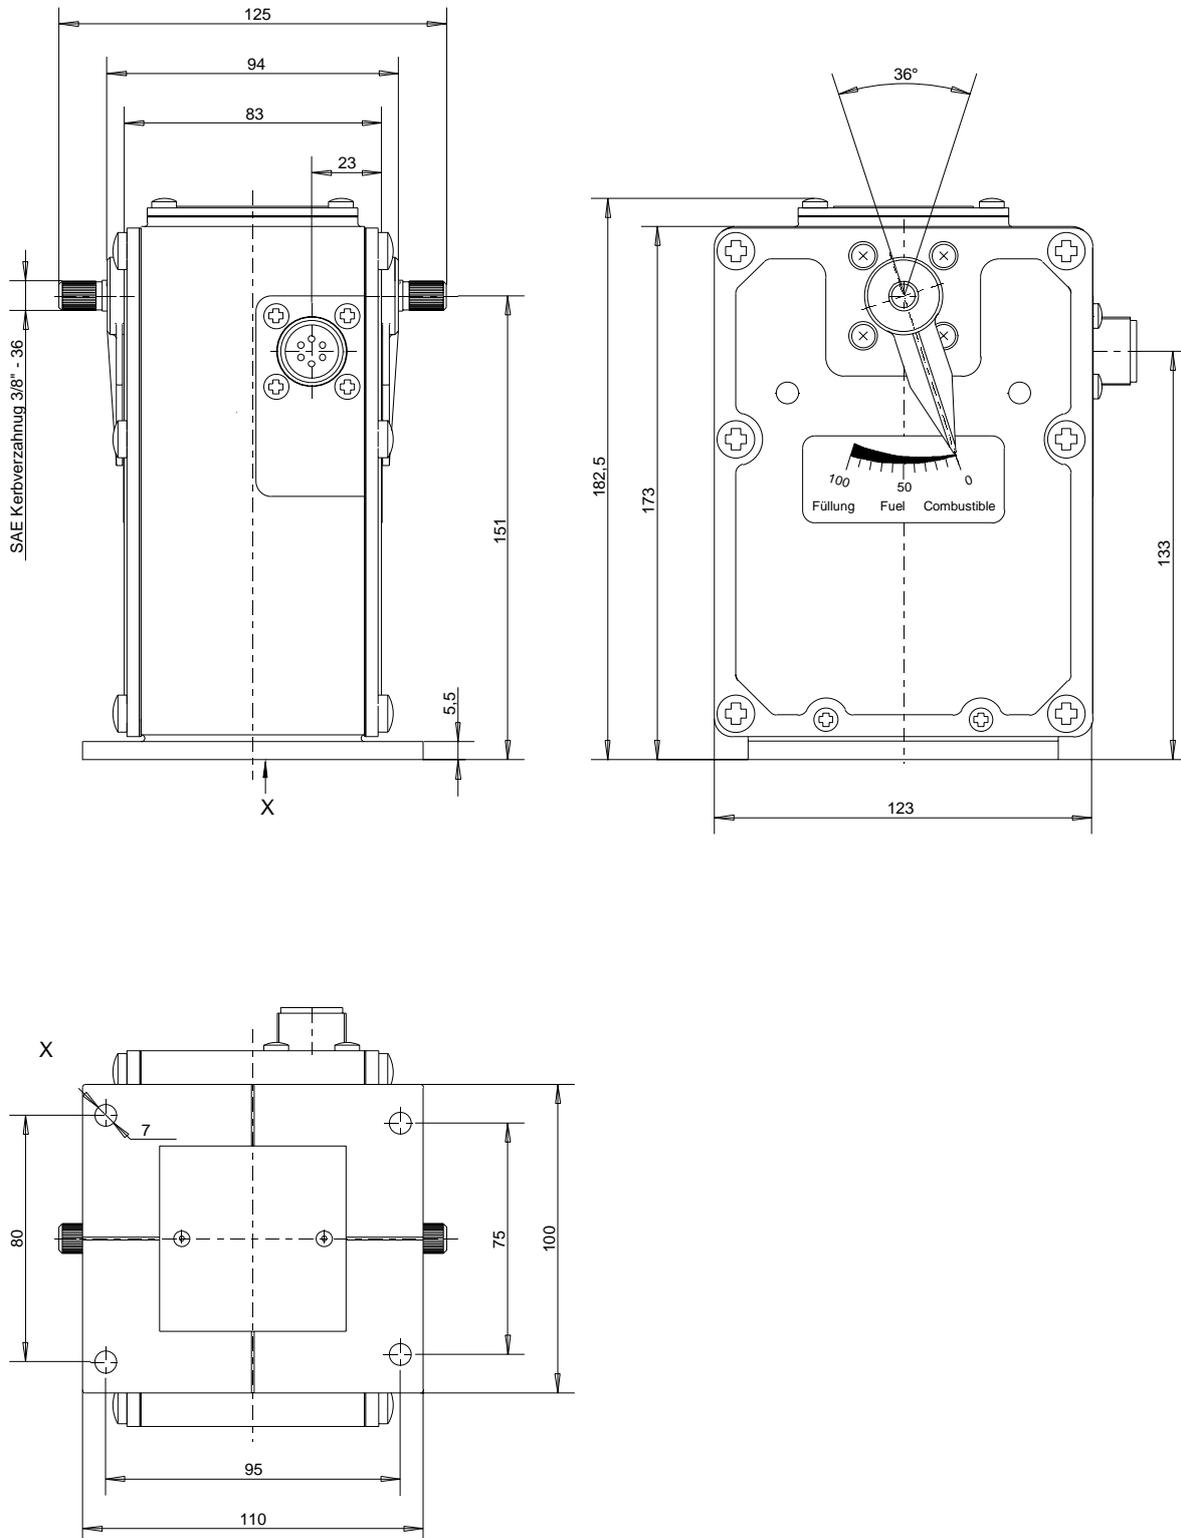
Maßzeichnung StG 6-01 und StG 6-02 V
